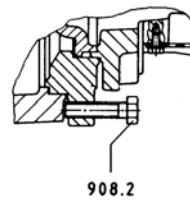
Abdrückschrauben bei Ausführung mit Zwischenring
